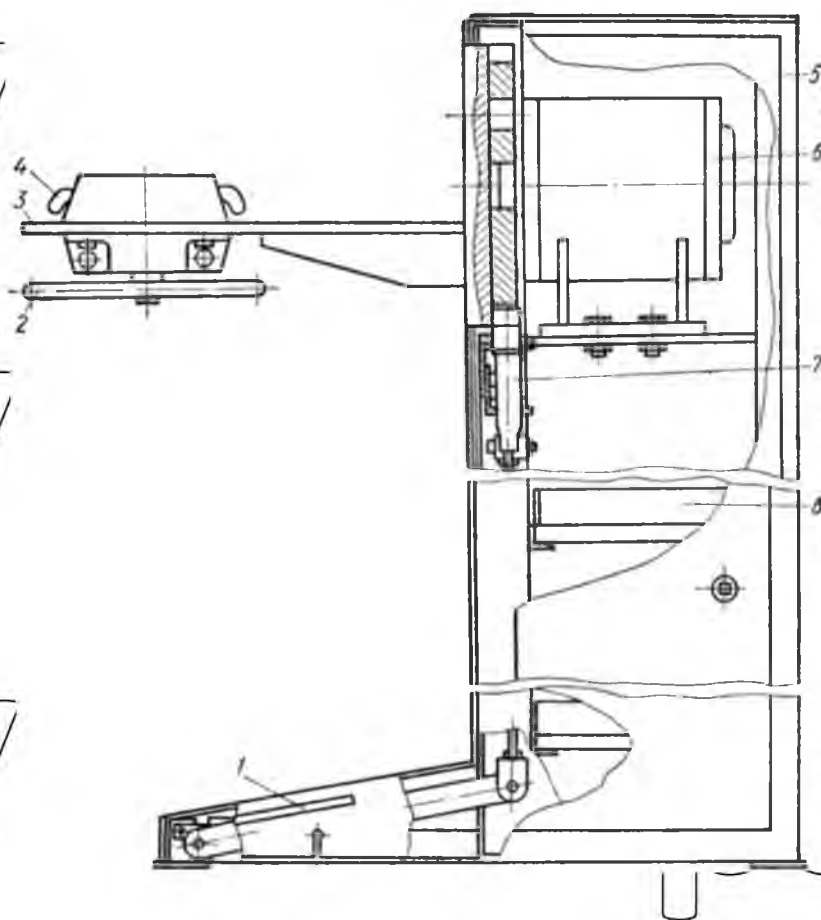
Схема стенда ОР-6283 для розбирання і складання колісних гальм: 1 — педаль; 2 — маховик; 3 — наладка; 4 — захват; 5 — рама; 6 — поворотний пристрій; 8 — полиця для інструменту
